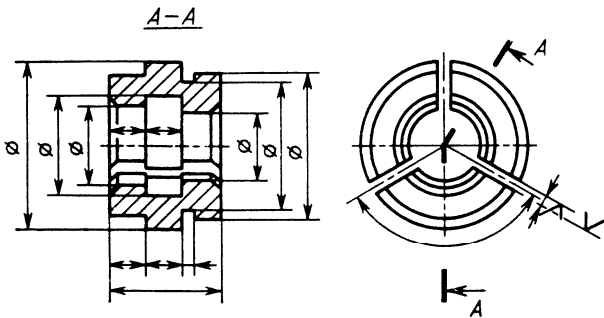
Оформление чертежа изделий, получаемых разрезкой заготовки на части
